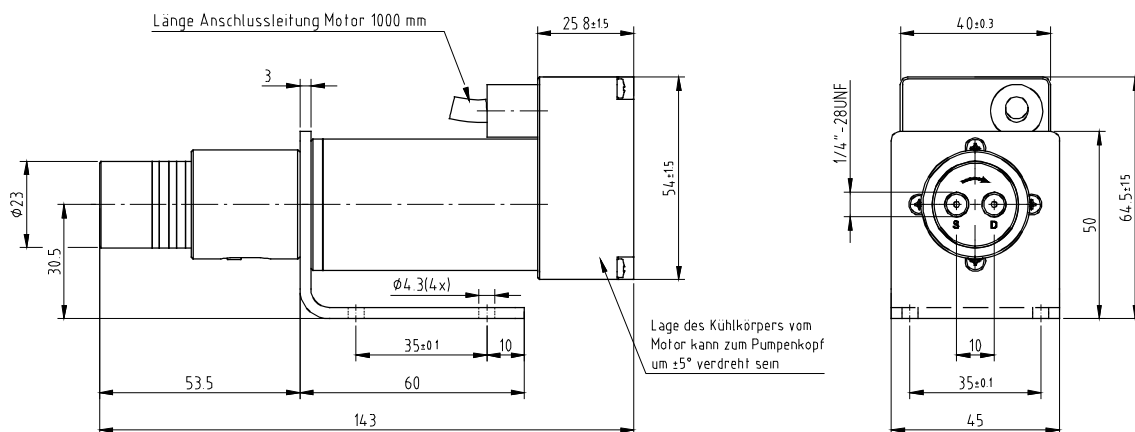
Abmessungen Mikrozahnringpumpe mzm-4605
